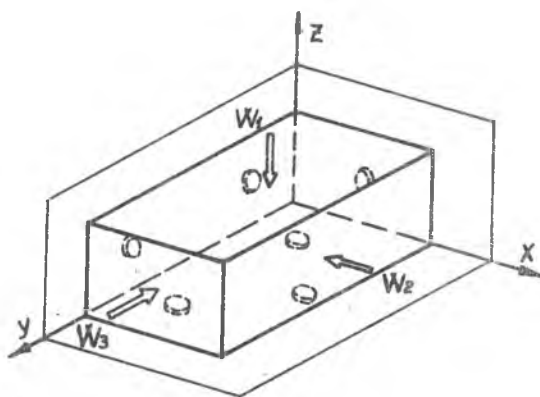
Схема базирования заготовки по плоским поверхностям.
